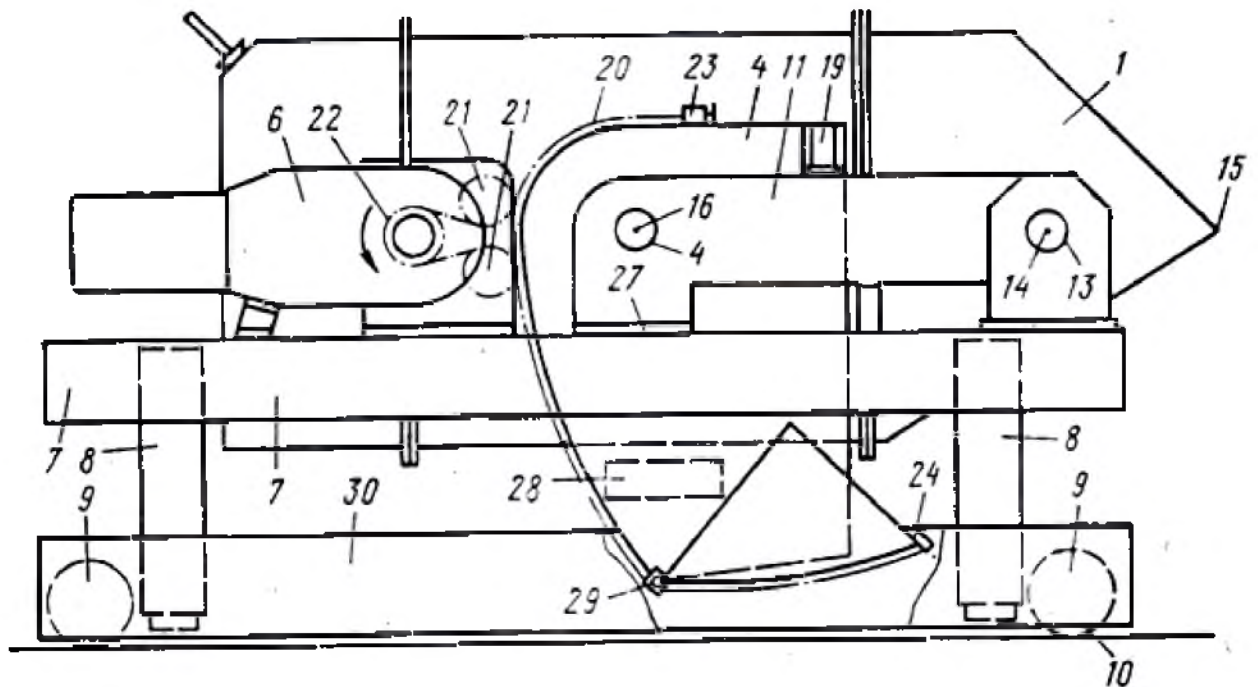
Пристрій для розливання розплавленого металу (вид збоку)
